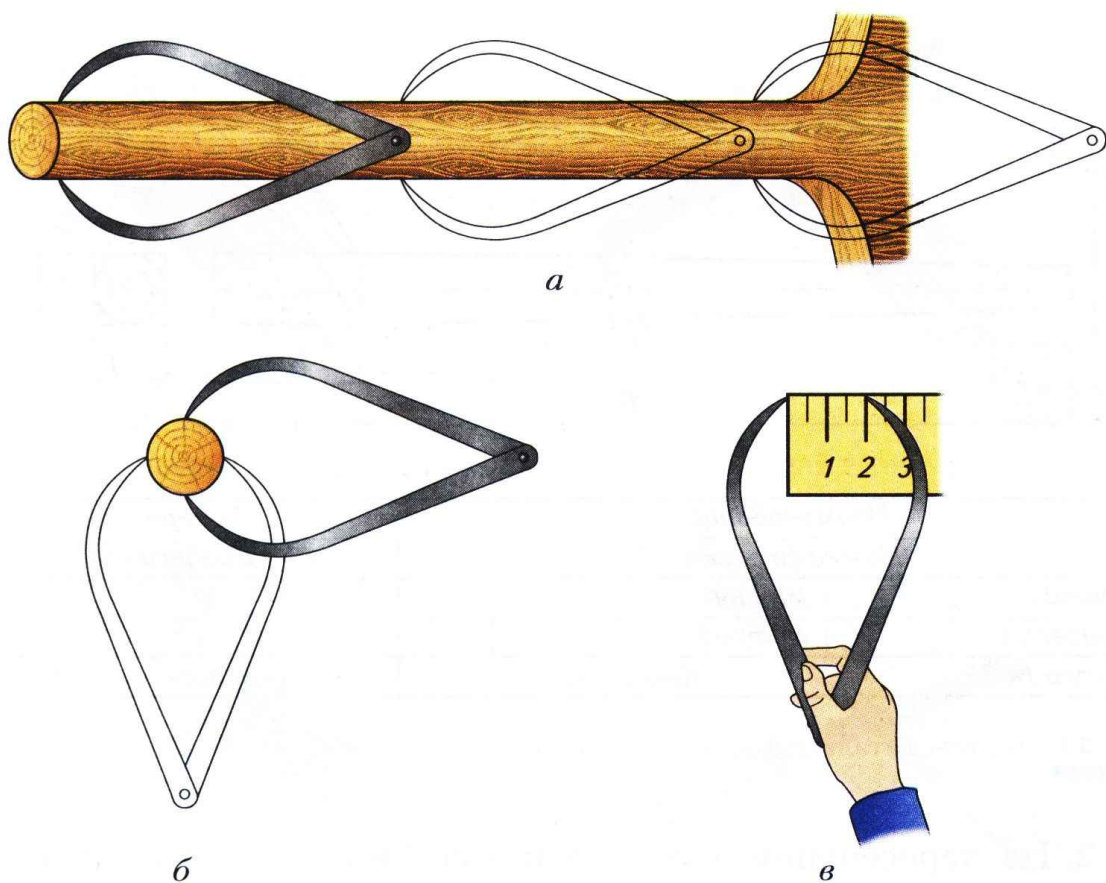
Контроль размеров цилиндрической части изделия: *а, б* – измерение размеров кронциркулем; *в* – отсчёт размера по линейке
